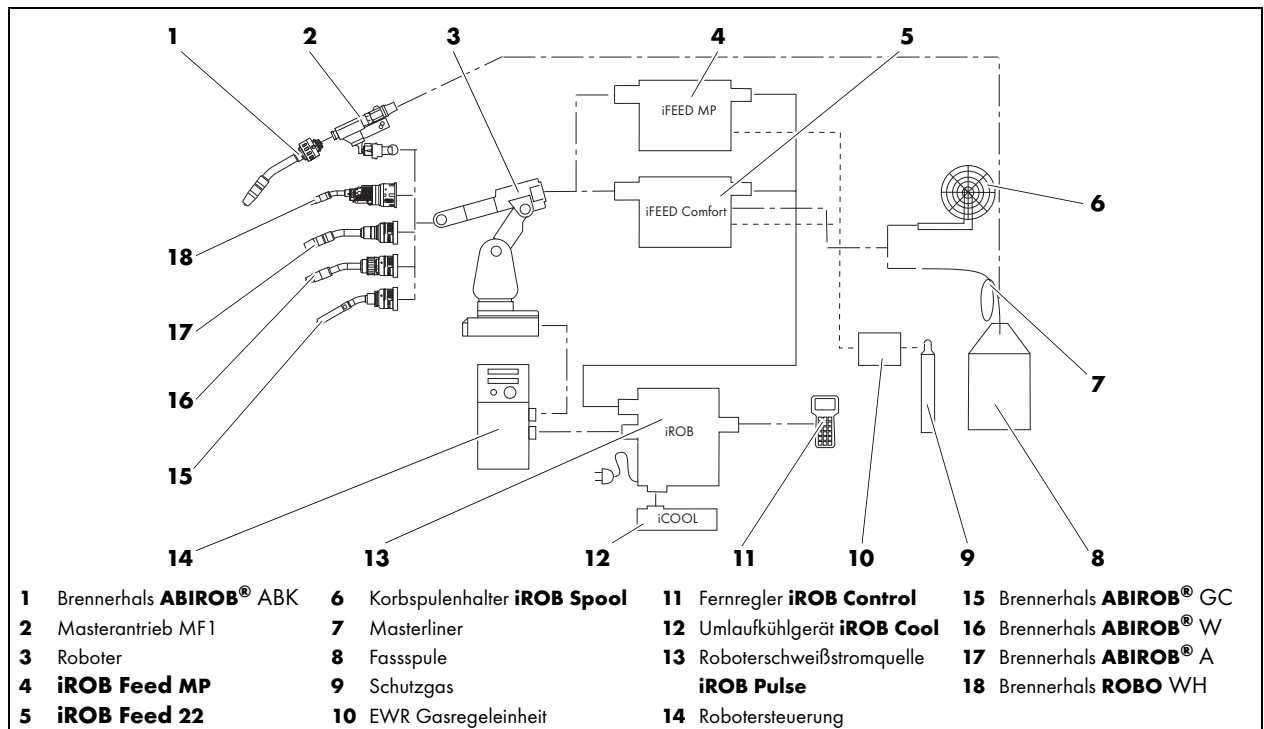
Komponenten Roboterschweißsausrüstung
